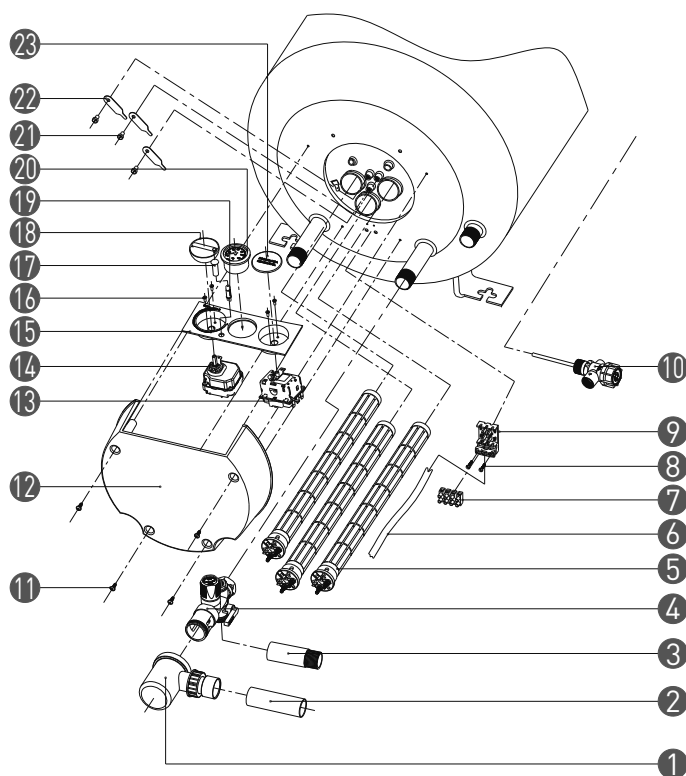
Montagem Grupo Eléctrico e Hidráulico
